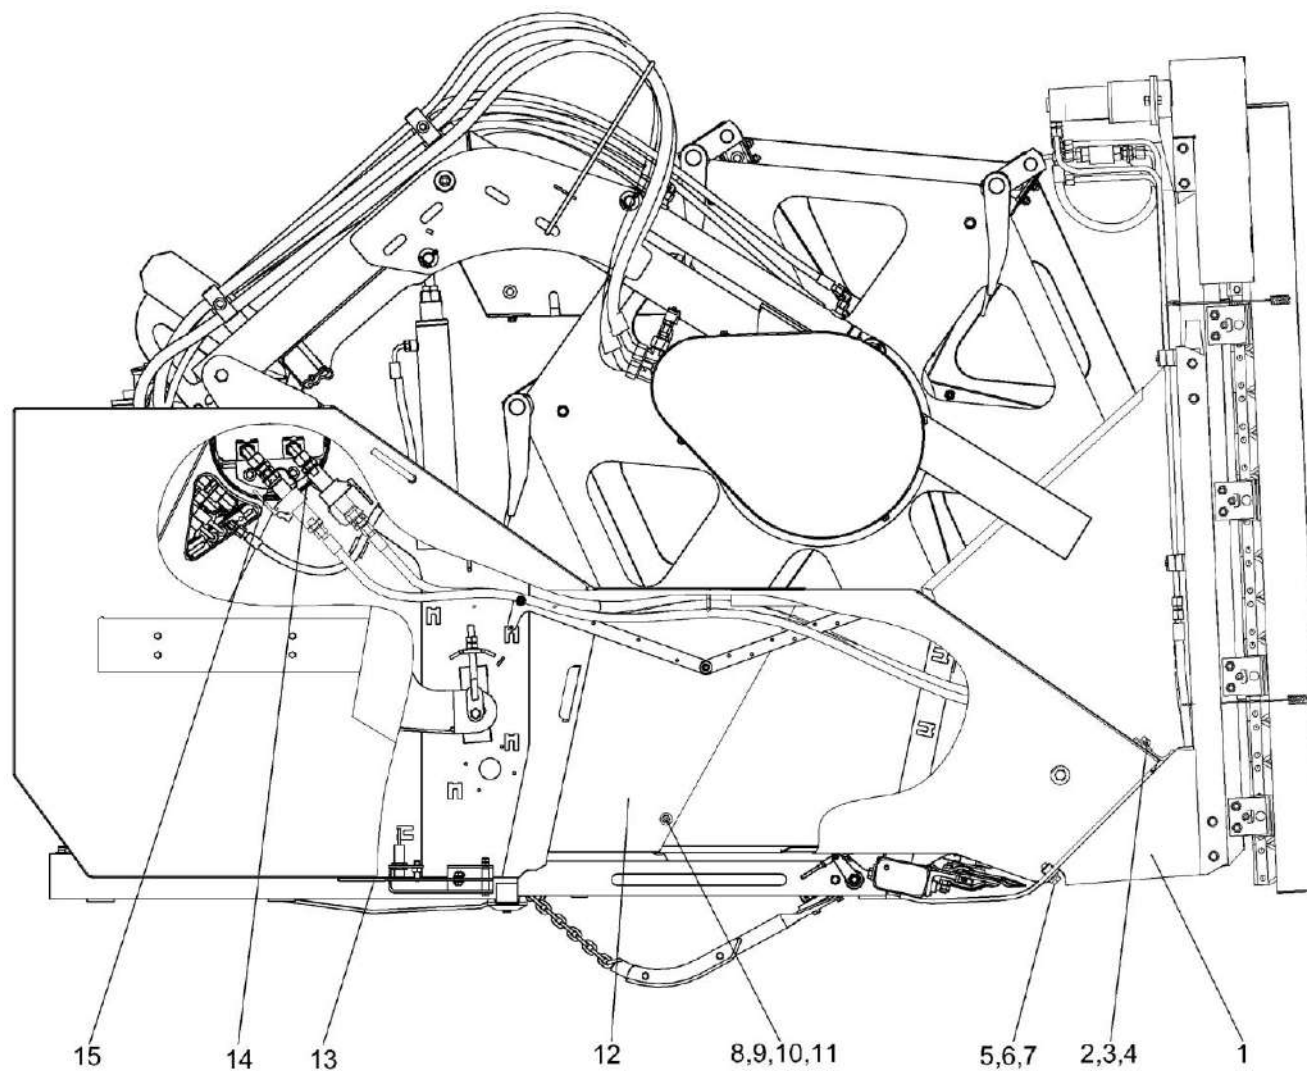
Демонтаж ремня привода режущего аппарата
